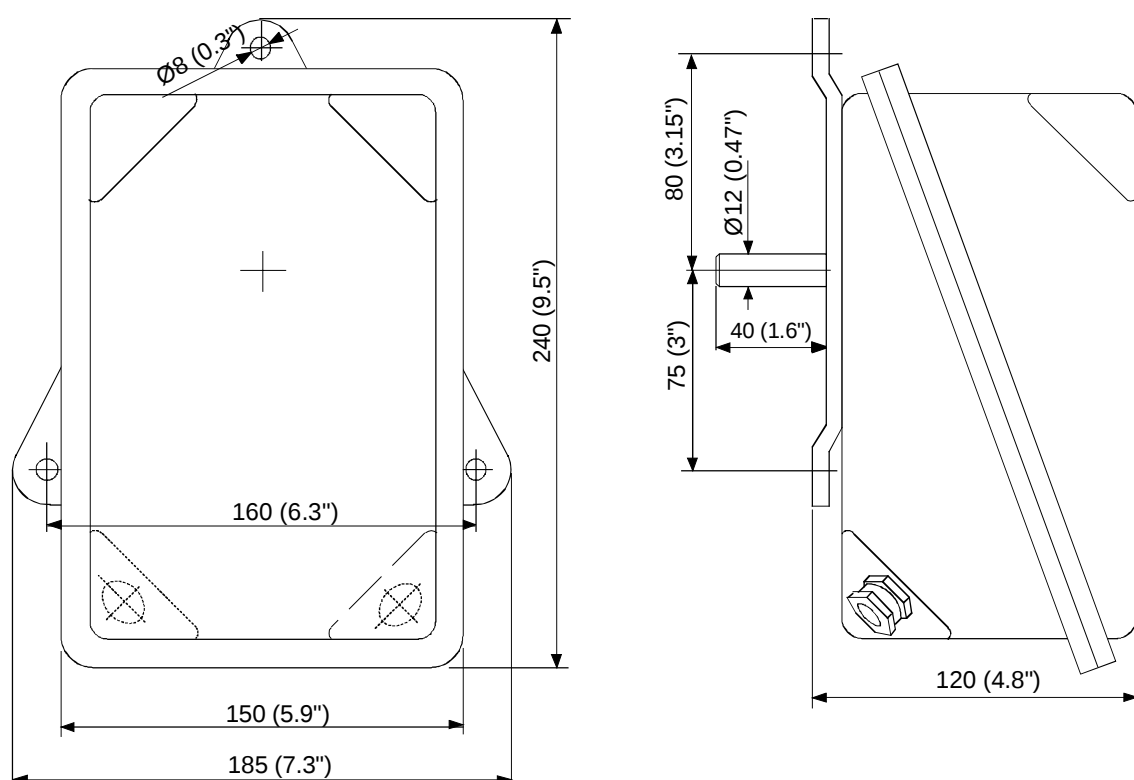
Dimensions du capteur d'angle de barre RF14XU
